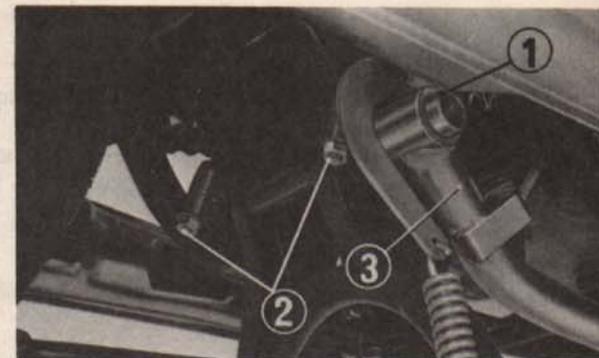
(1) Fourreau métallique de pivot de béquille principale
